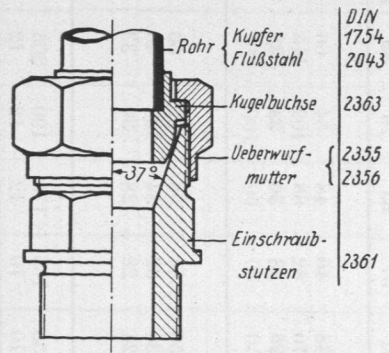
Einschraubverschraubung, schwer, nach DIN 2360.
